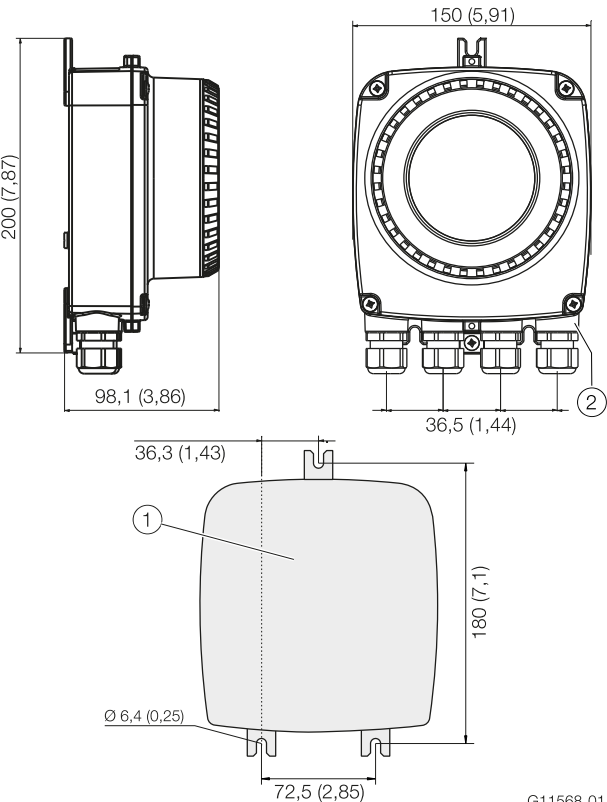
Монтажные размеры однокамерного корпуса G11568-01
